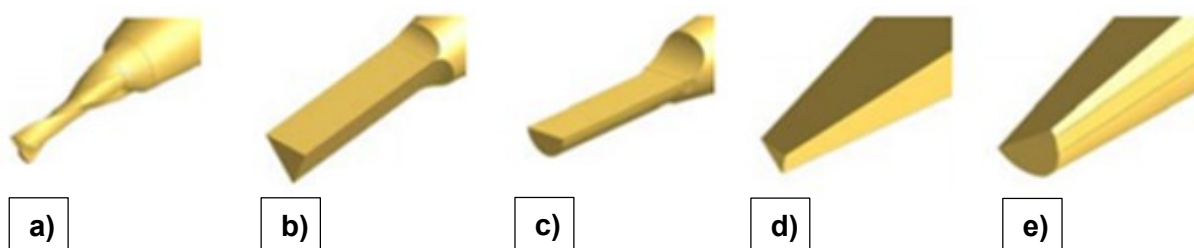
Diferentes formas geométricas para ferramentas de microusinagem (FANG et al., 2003)
